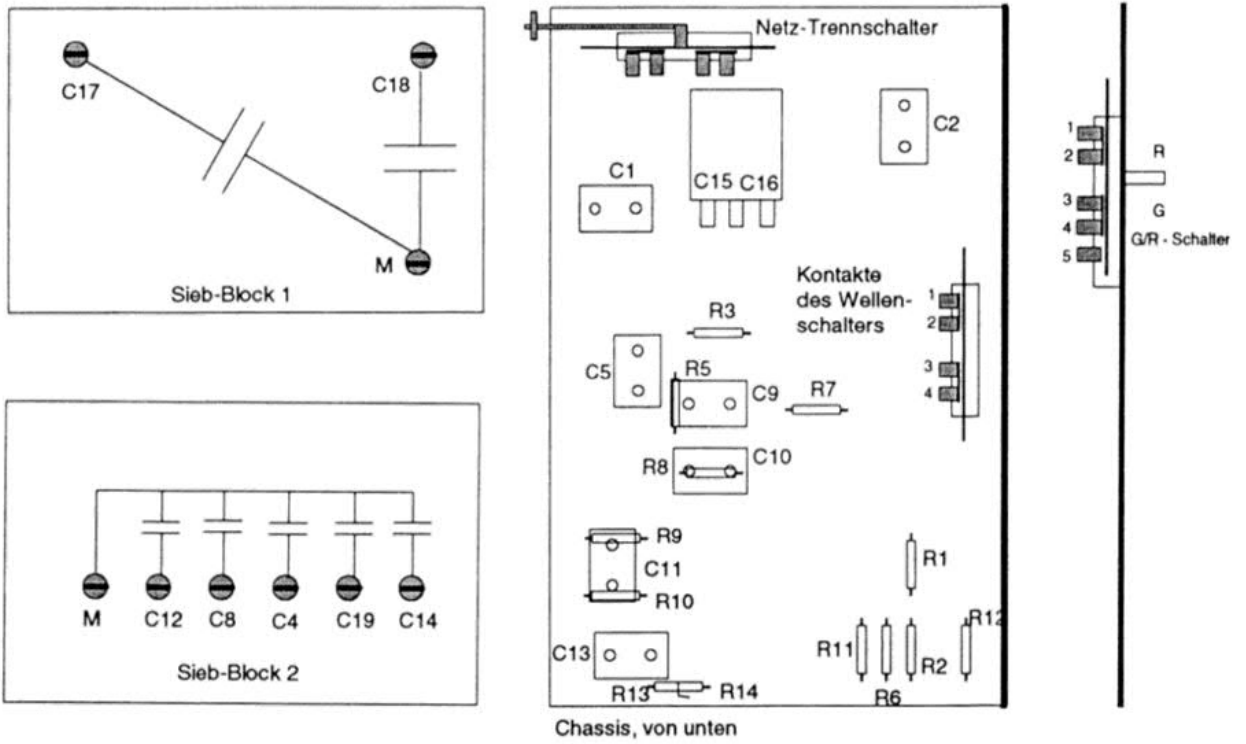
Lageplan der Bauteile unter dem Chassis des OWIN E 22 W
